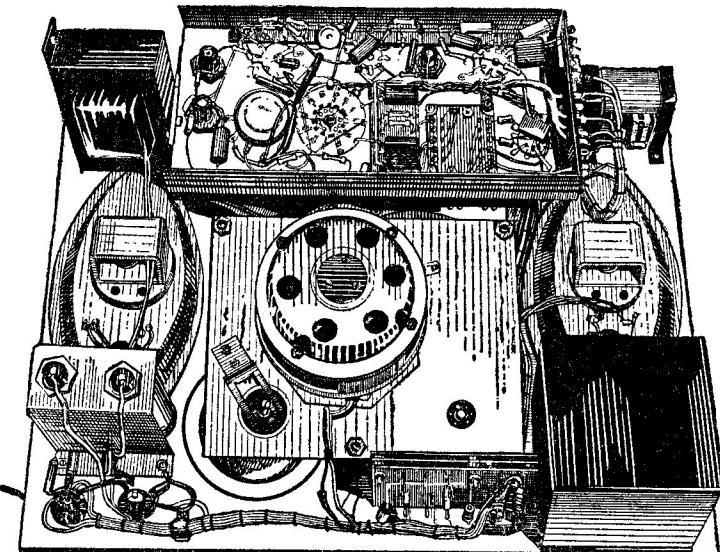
Расположение деталей лентопротяжного механизма и усилителя снизу панели
